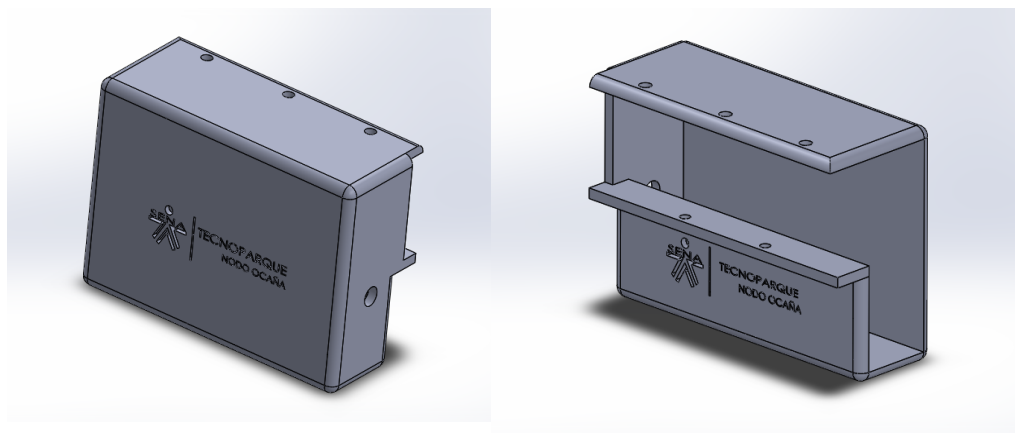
Diseño del CAD en 3D de la estructura del motor. *Fuente: Autor.
